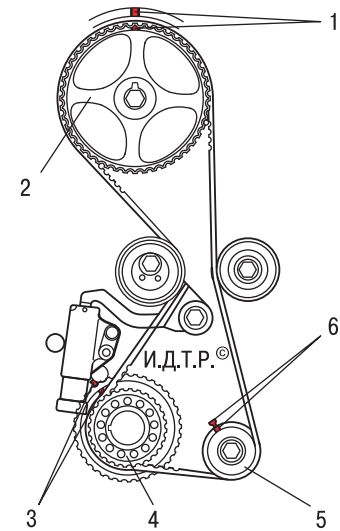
Установочные метки на зубчатых шкивах привода распределительного вала двигателя: 1 – метки на шкиве распределительного вала; 2 – зубчатый шкив привода распределительного вала; 3 – метки на шкиве коленчатого вала; 4 – зубчатый шкив коленчатого вала; 5 – зубчатый шкив привода масляного насоса; 6 – метки на шкиве привода масляного насоса
